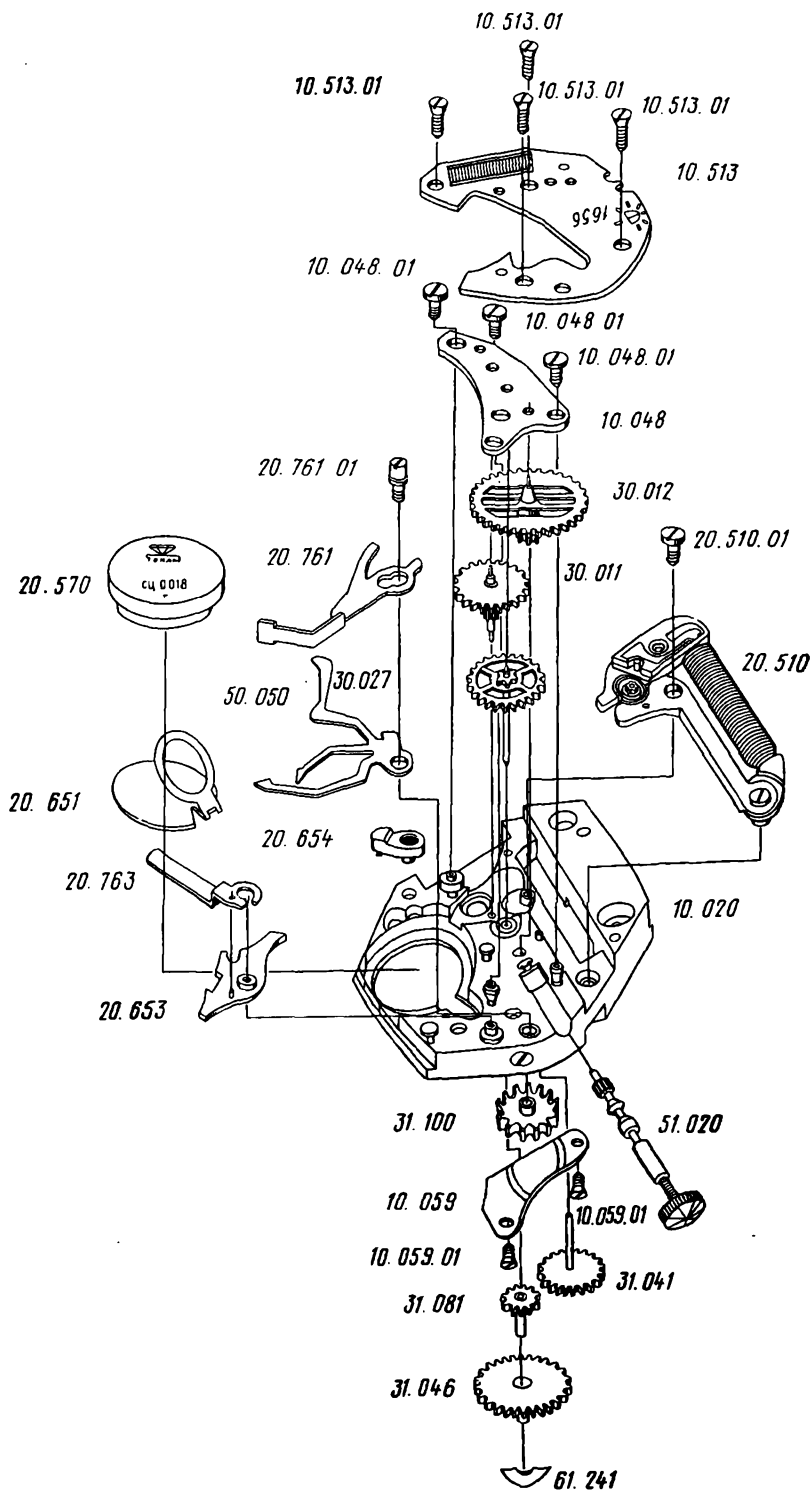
Детали и сборочные единицы механизма часов 1656:
